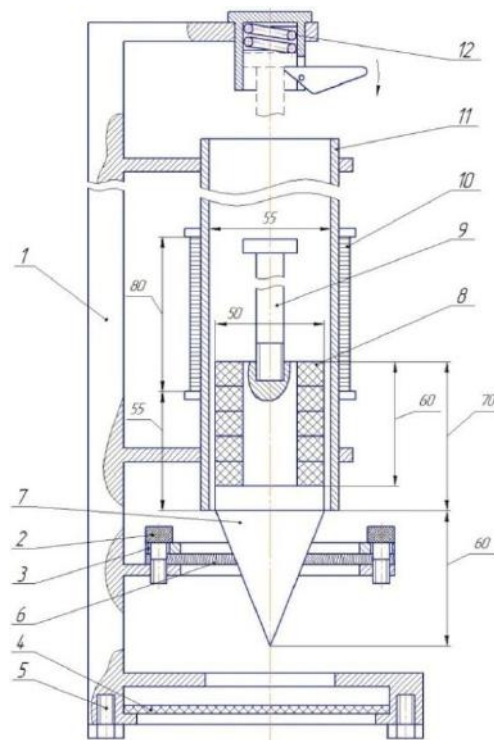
Схема установки (устройства): 1 – стойка испытательного прибора;
